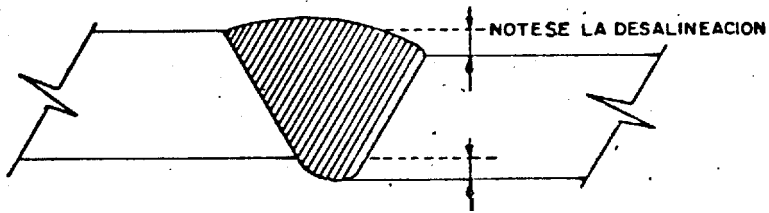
CONDICION DESALINEAMIENTO (Ref. 9)
